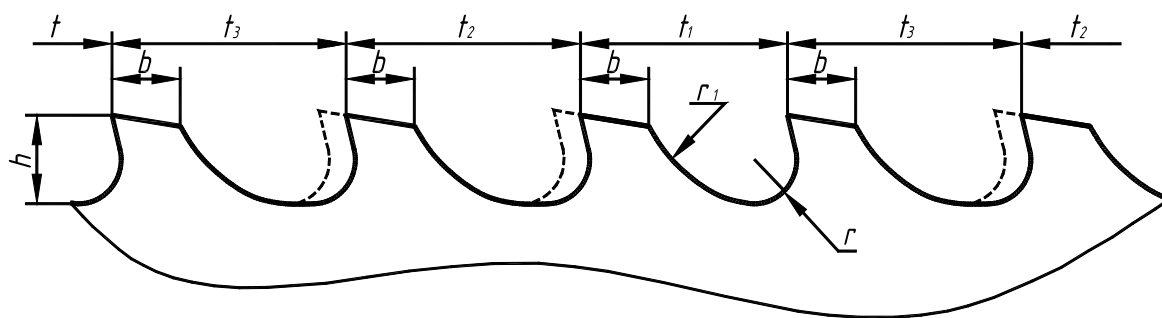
Форма и основные размеры профиля чистовых и калибрующих зубьев с неравномерными шагами круглой протяжки
